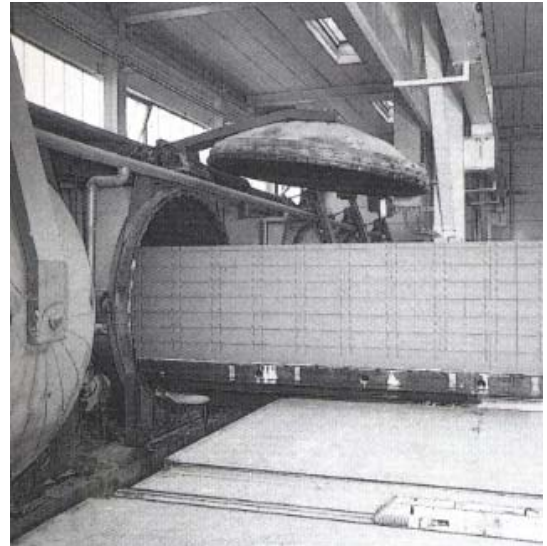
Dampfhärtung von Porenbetonsteinen, aus [1].
